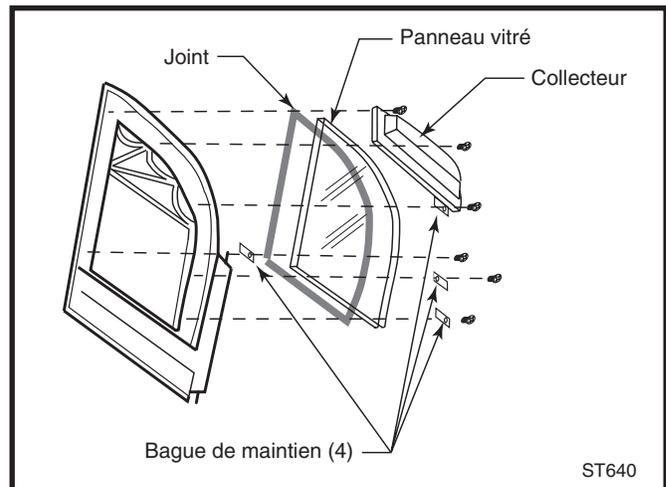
Vue éclatée de l'ensemble de glace de la porte gauche.
